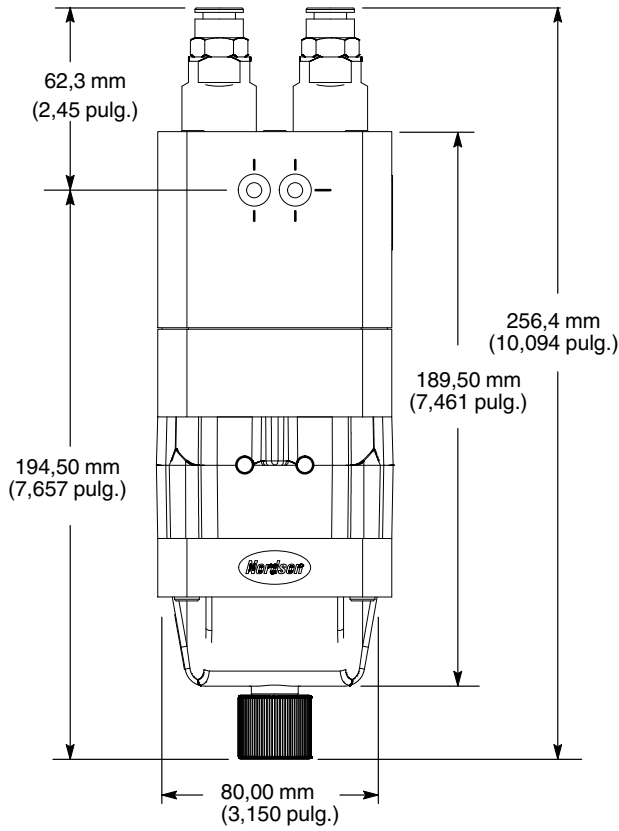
Dimensiones de la bomba estándar Prodigy HDLV
